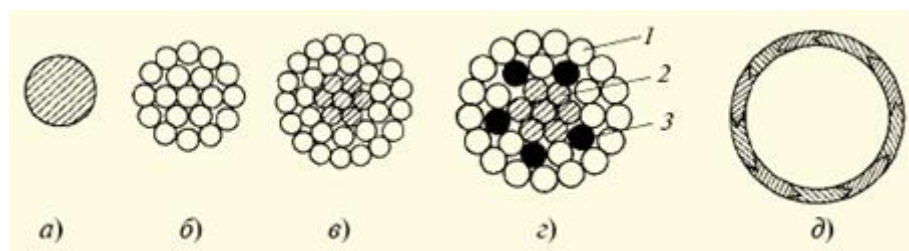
Конструкция неизолированных проводов: а – однопроволочный; б – многопроволочный из одного металла (сплава); в – многопроволочный из двух металлов (сталеалюминиевый); г – расширенный; д – пустотелый (полый); 1 – алюминий; 2 – сталь; 3 – наполнитель
